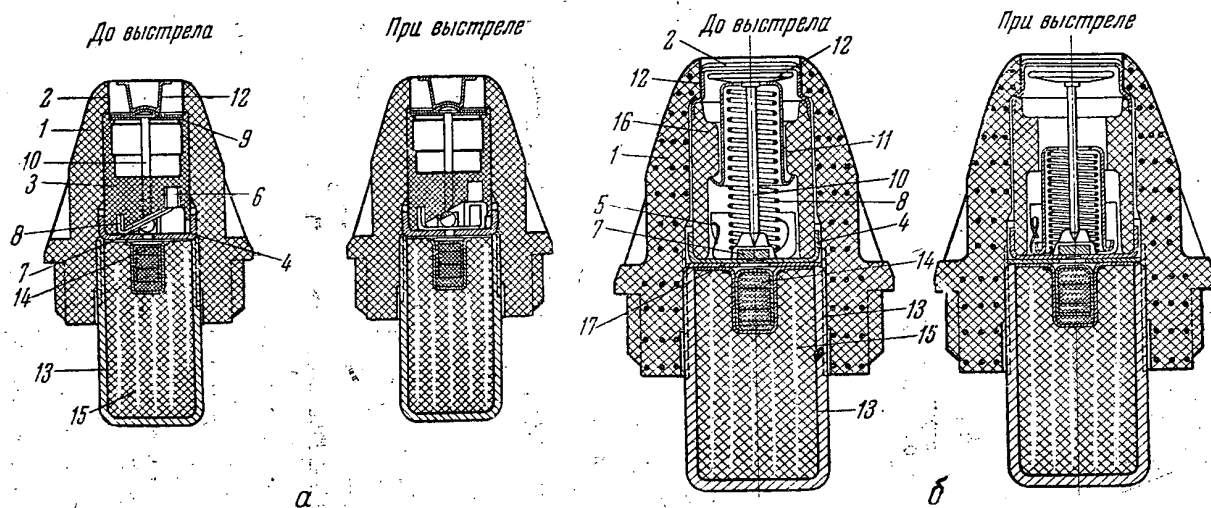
Взорыватели: а — взрыватель МП-82; б — взрыватель М-2: 1 — корпус; 2 — мембрана; 3 — втулка; 4 — чашечка; 5 — предохранительная гильза; 6 — цилиндр; 7 — предохранитель; 8 — пружина; 9 — диафрагма; 10 — ударник с жалом; 11 — оседающая гильза; 12 — колпачок; 13 — стакан детонатора; 14 — капсюль-детонатор; 15 — детонатор; 16 — втулка; 17 — опорная шайба
